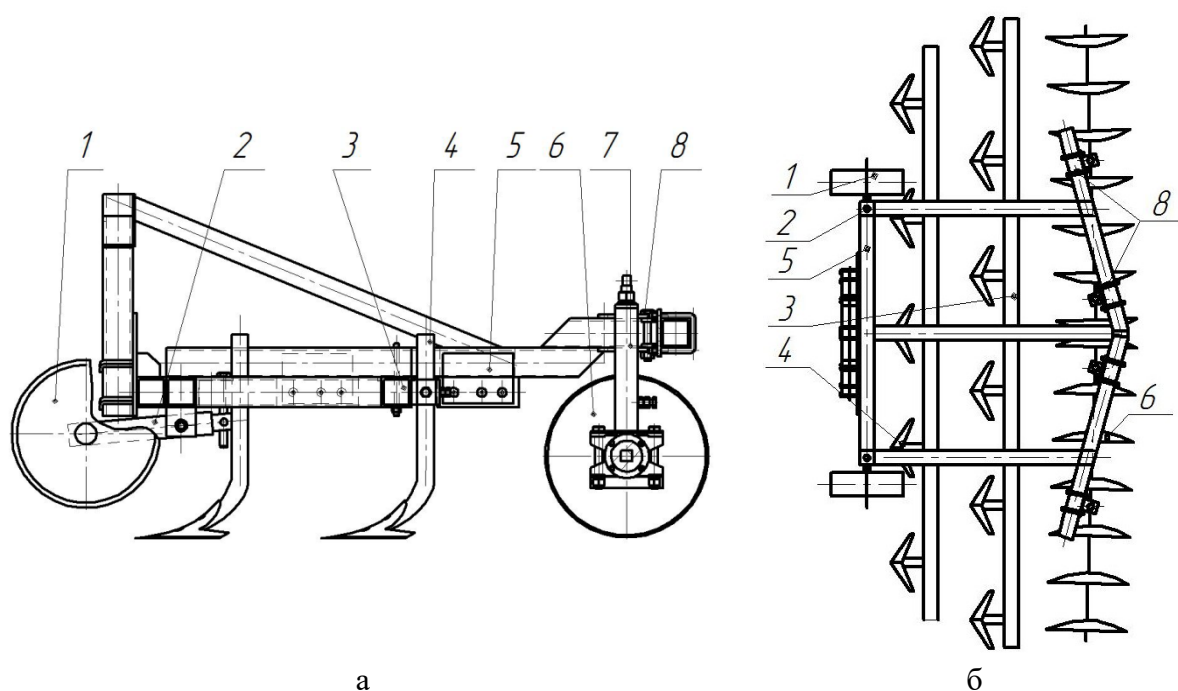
Вариант почвообрабатывающего агрегата для мелкой и поверхностной почвообработки (а), схема размещения рабочих органов при минимальном угле атаки (б): 1 - колесо опорное; 2 - механизм регулировки положения опорных колес; 3 - брус съёмный; 4 - лапы культиваторные; 5 - рама; 6 - секции дисковые; 7 - механизм регулировки положения дисковой секции; 8 - кронштейн крепления дисковой секции
